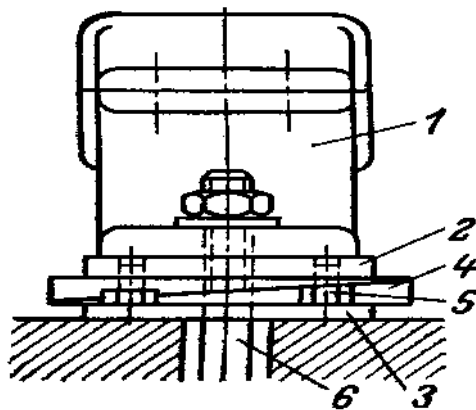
Установка подшипникового стояка на отдельной фундаментной плите;
